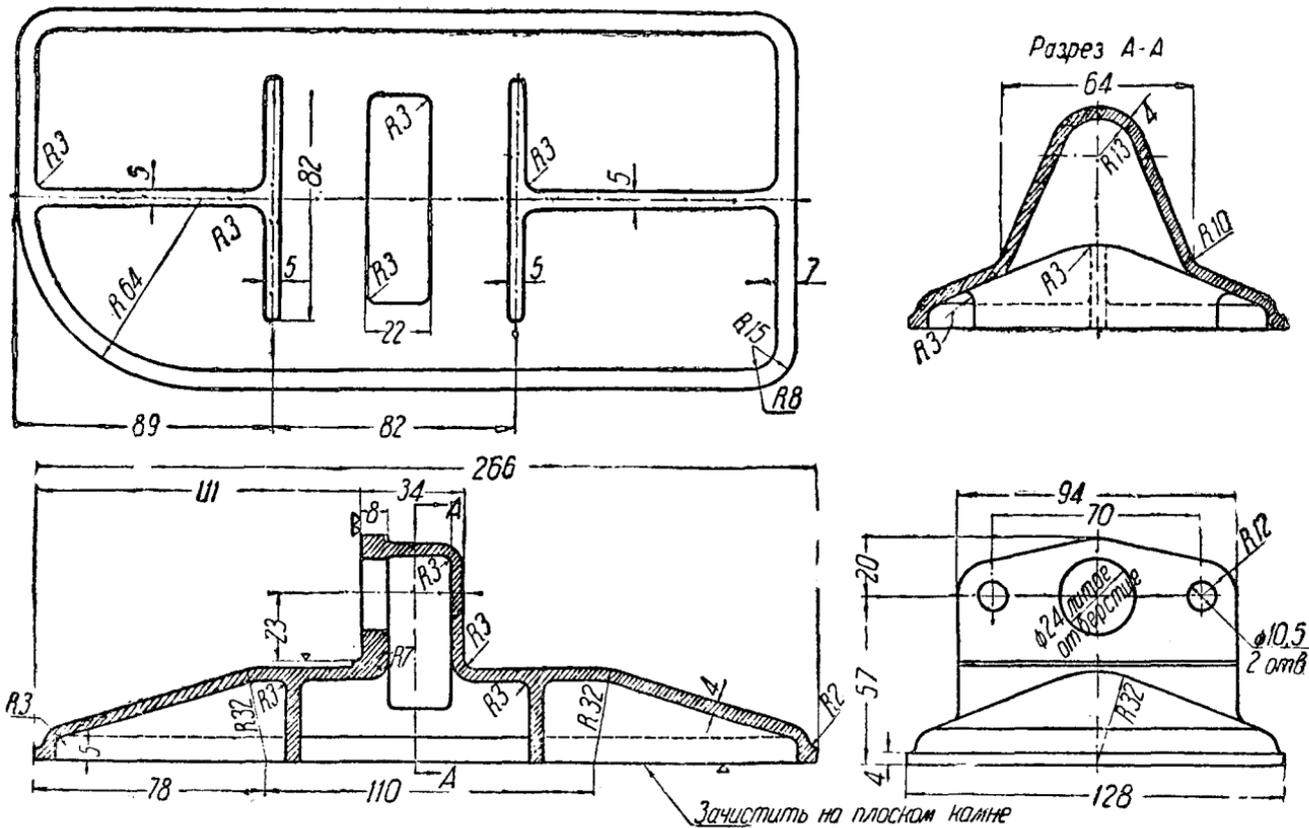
Дет. № 0989. Корпус маслоприёмника заднего
